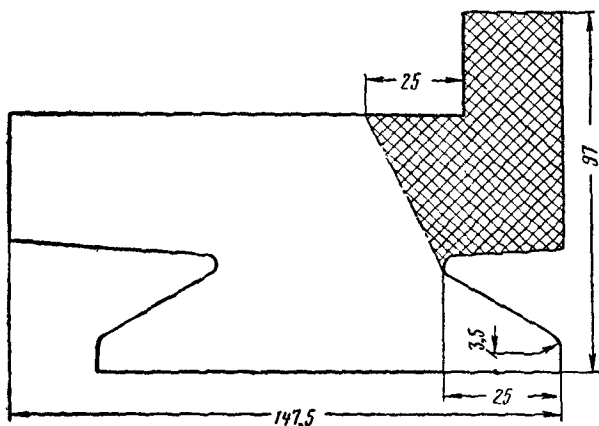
Заготовка медной пластины коллектора НБ-411 (заштрихованная часть — поверхность хромирования)
